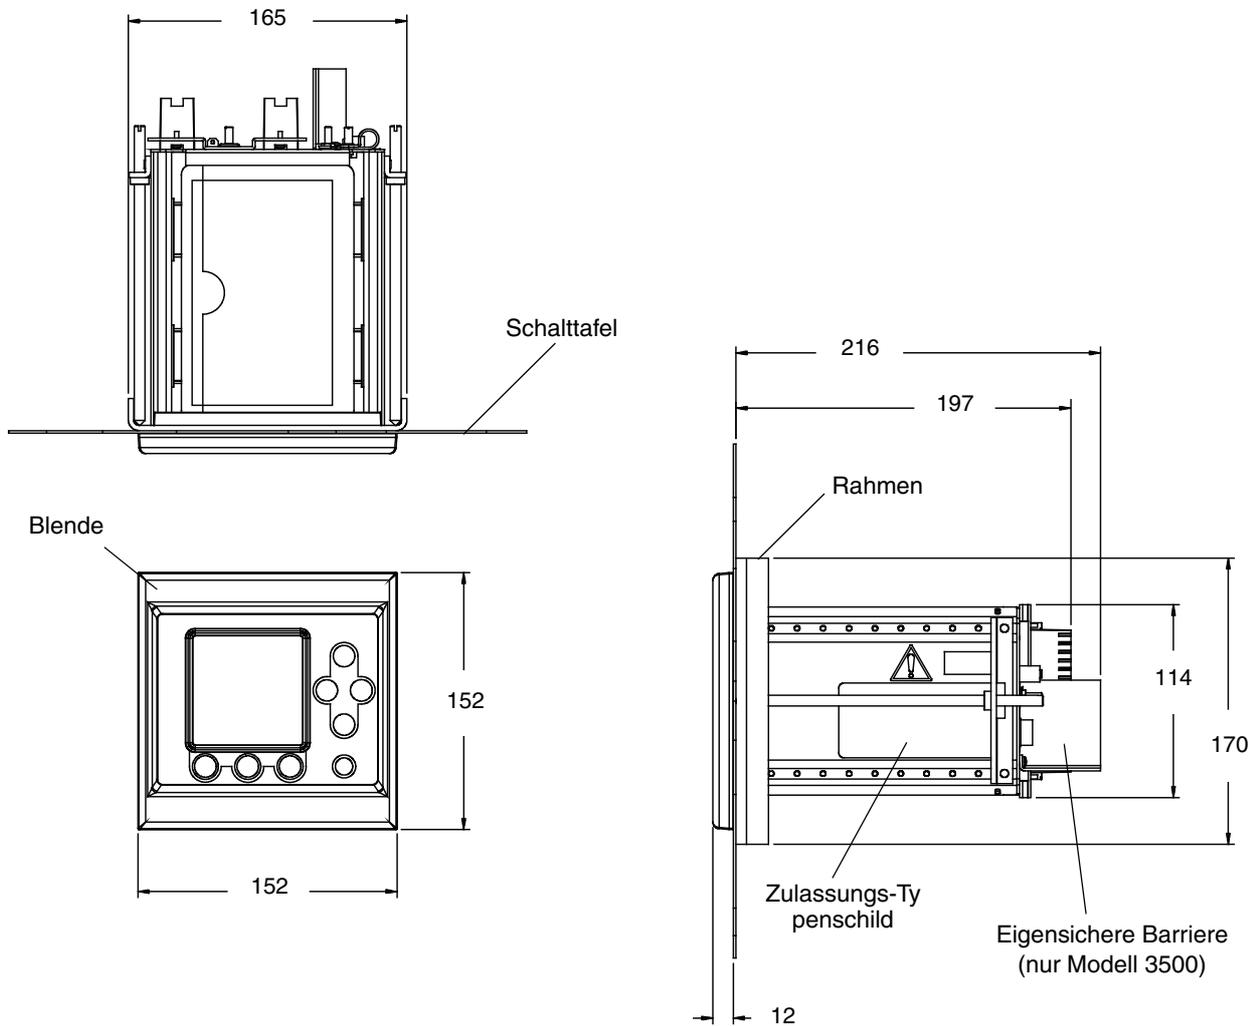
Abmessungen Modell 3300 oder 3500, Schalttafelmontage mit Ein-/Ausgangskabel
